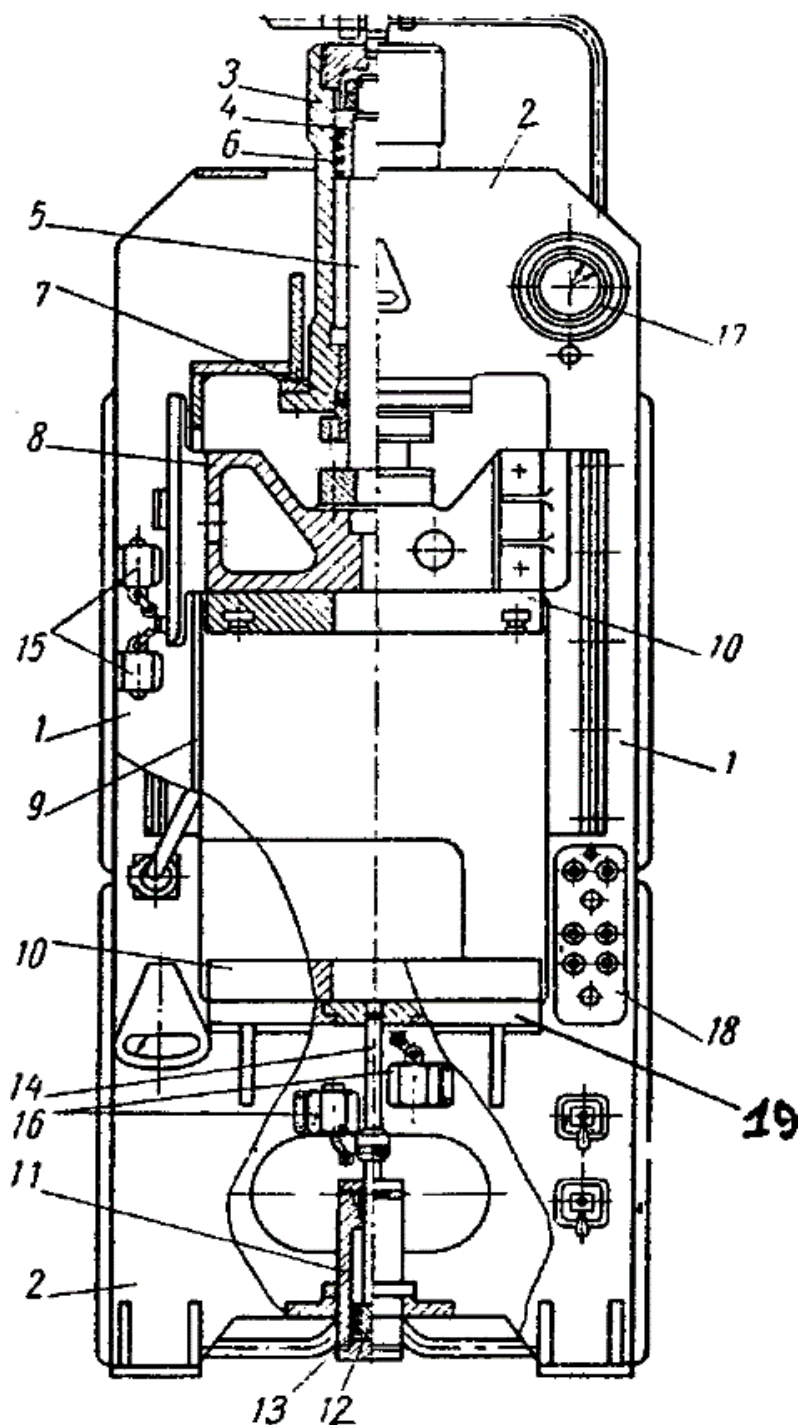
Рамный гидравлический пресс: 1 – стойки; 2 – плиты; 3 – главный гидроцилиндр; 4 – дифференциальный плунжер; 5 – шток; 6, 7 – уплотнительные манжеты; 8 – подвижная верхняя плита; 9 – направляющие; 10 – верхняя и нижняя рабочие плиты; 11 – гидроцилиндр выталкивателя; 12 – дифференциальный плунжер выталкивателя; 13 – уплотнительные манжеты; 14 – шток выталкивателя; 15 – конечные выключатели (ограничители хода) верхней плиты; 16 – конечные выключатели хода выталкивателя; 17 – электроконтактный манометр давления; 18 – пульт управления пресса; 19 – стол
